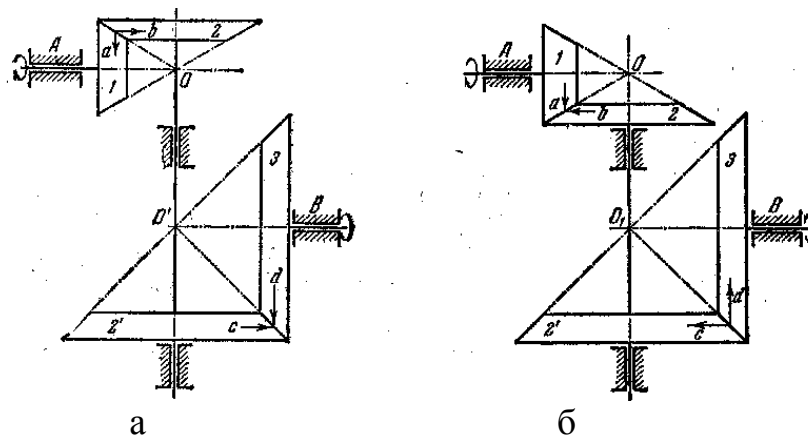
Схема двухступенчатой конической передачи:
